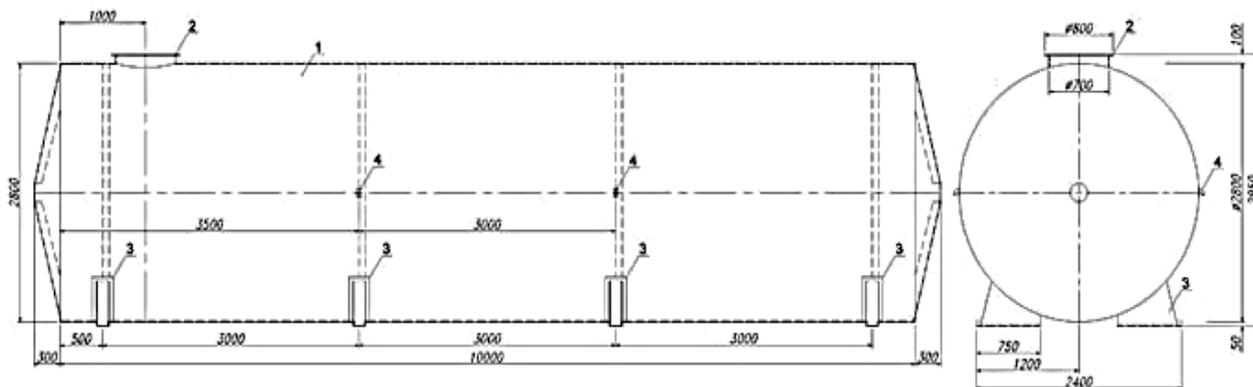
Схема горизонтального биореактора с использованием резервуара РГС-60[5]:
